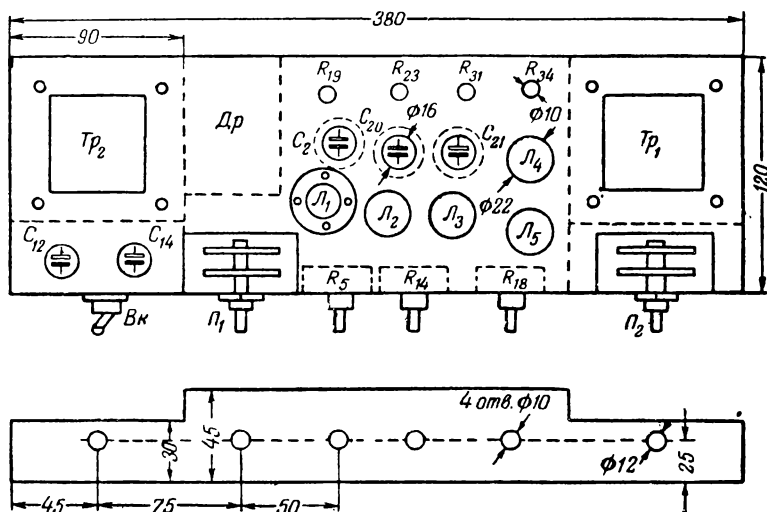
Расположение деталей на шасси стационарного усилителя.
